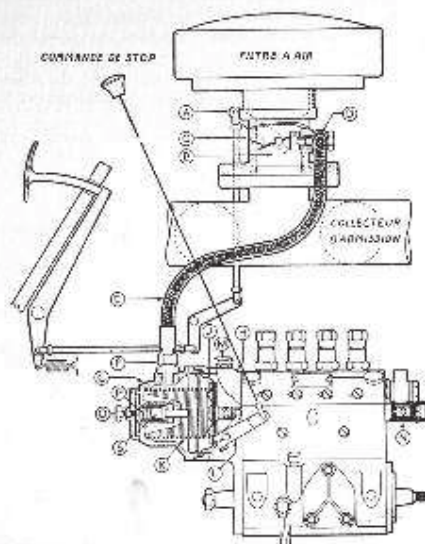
Installation de la pompe d'injection et coupe du régulateur et du venturi.
